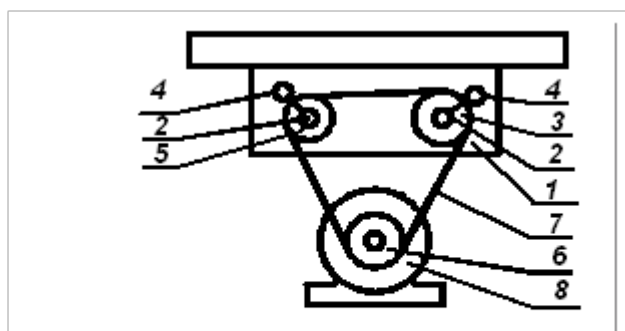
Вибровозбудитель: 1 – корпус; 2 – валы; 3, 5 – шкивы вибровозбудителя; 4 – дебалансы; 6 – шкив электродвигателя; 7 – клиноременная передача; 8 – электродвигатель
